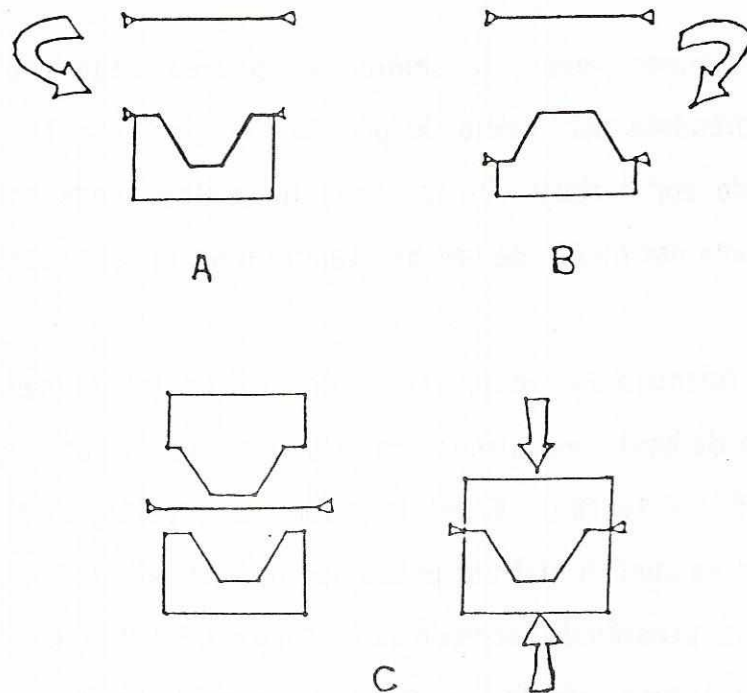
Definiciones de configuraciones de moldes. A: Molde hembra (formado negativo). B: Molde macho (Formado positivo). C: Combinación de un molde macho.
